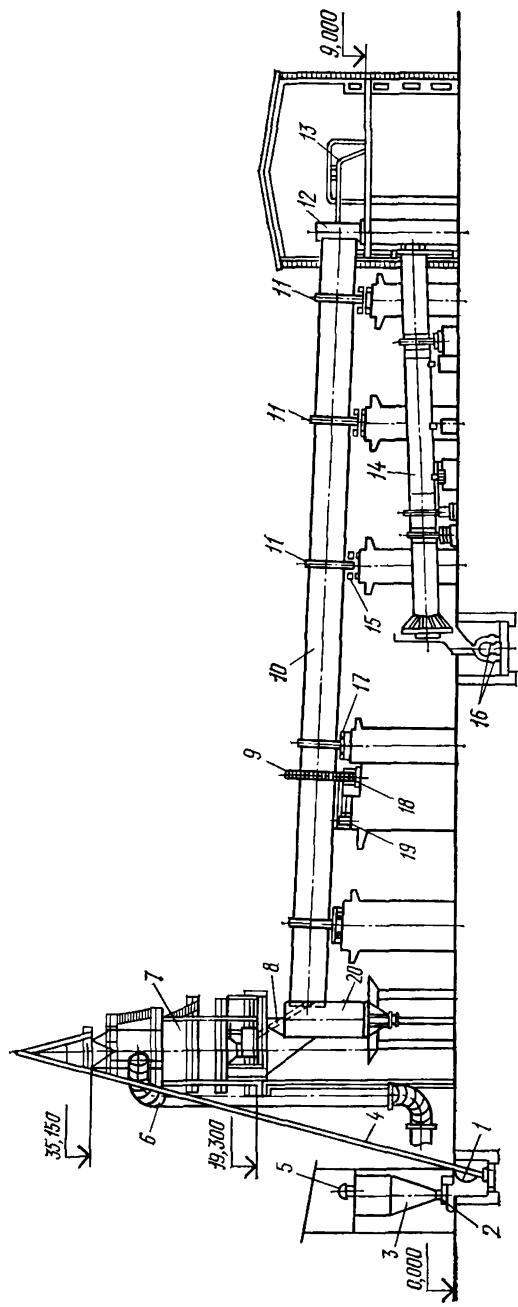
Короткая вращающаяся печь с шахтным подогревателем известняка и однобаранным ходильником известнико:
